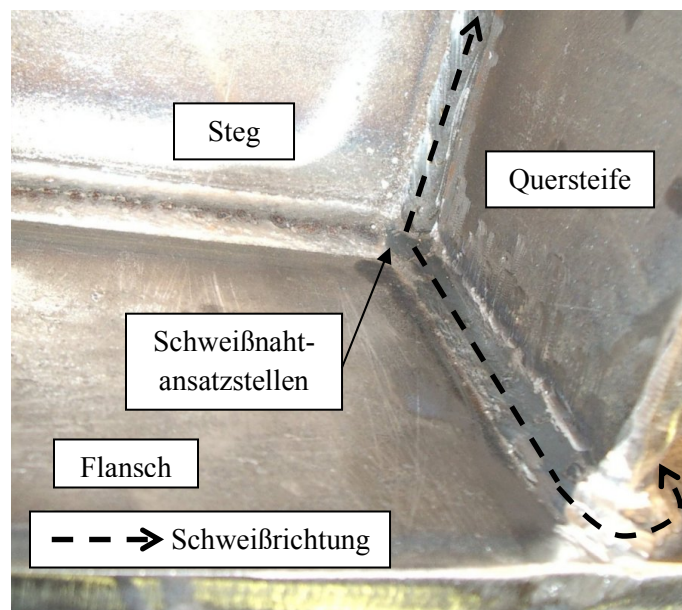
Schweißanweisung für eingepasste Quersteife
